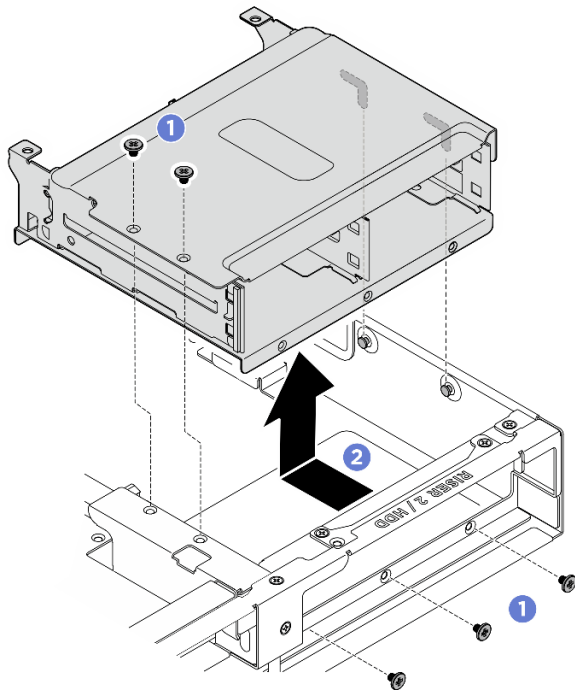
Entfernen der hinteren Laufwerkhalterung
